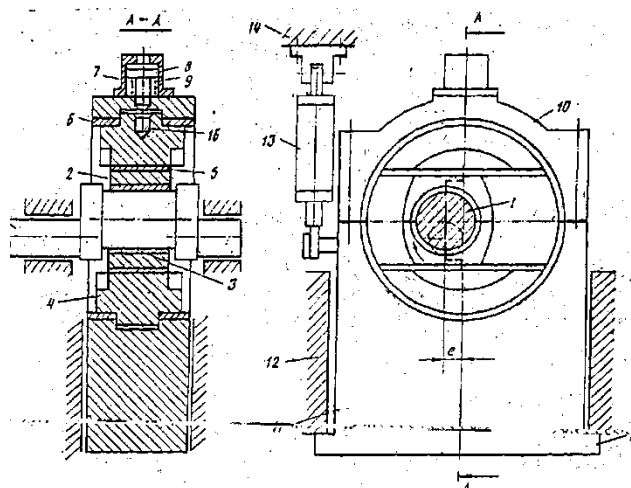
Схема безмуфтового пресса с кулисным механизмом
